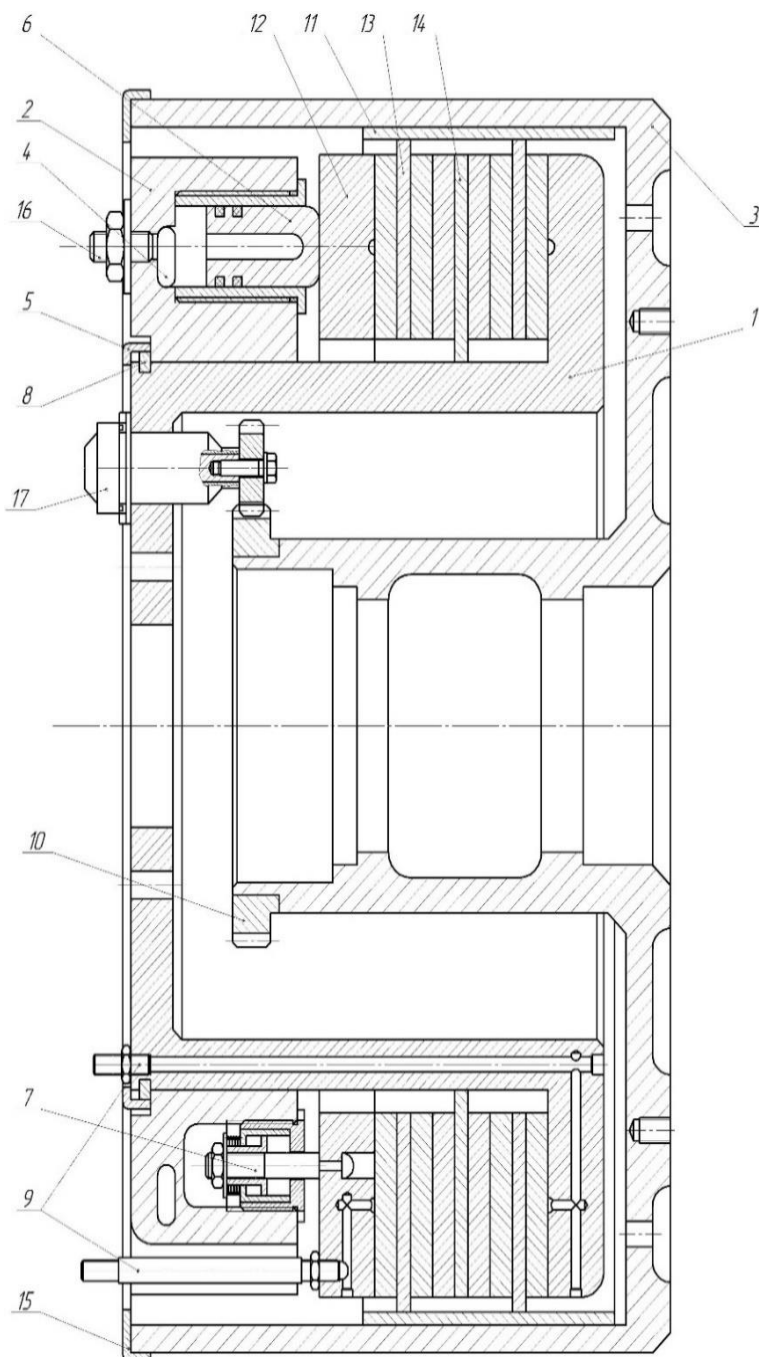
Тормозное устройство (Патент №107834) 1 – корпус; 2 – блок цилиндров; 3 – тормозной барабан; 4 – кольцевой канал; 5 – крышка;
